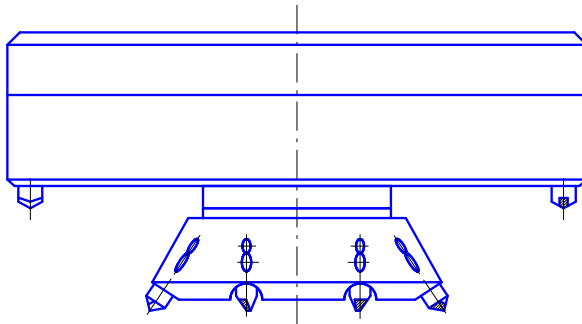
Принципова схема двоступінчастої комбінованої фрези
